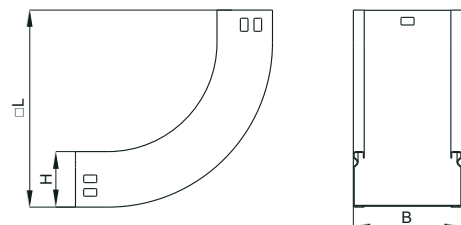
Поворот плавный на 90° вертикальный внутренний / Figure B.2 – 90° vertical internal smooth bend
